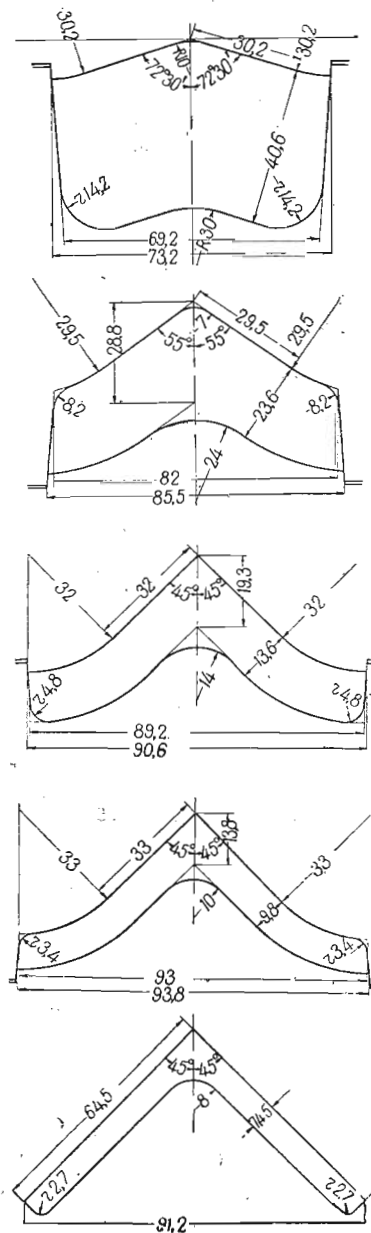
Калибровка равнобокого углового профиля № 6,5
